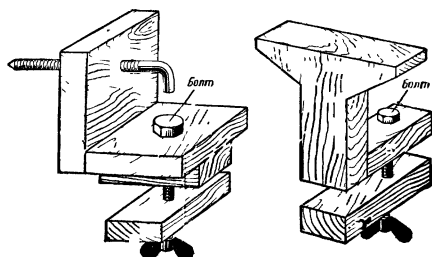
Крепление задней бабки и подручника болтами с прижимными гайками
